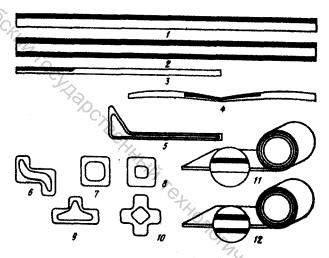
Поперечные сечения профилей сварных конструкций:
